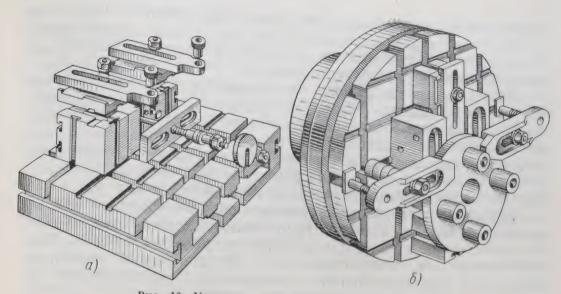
Универсально-сборные приспособления: a — сборный кондуктор для сверления отверстий; b — патрон для токарной обработки с эксцентричной установкой изделия
